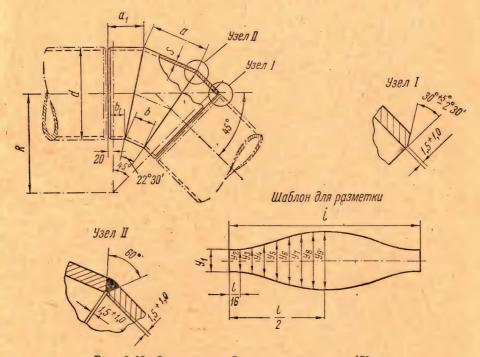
Отвод сварной с углом поворота 45°.
